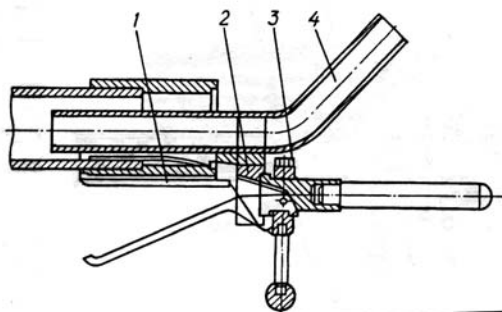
Устройство для очистки насосно- компрессорной трубы со сквозным осевым отверстием внутри парафиновых отложений
